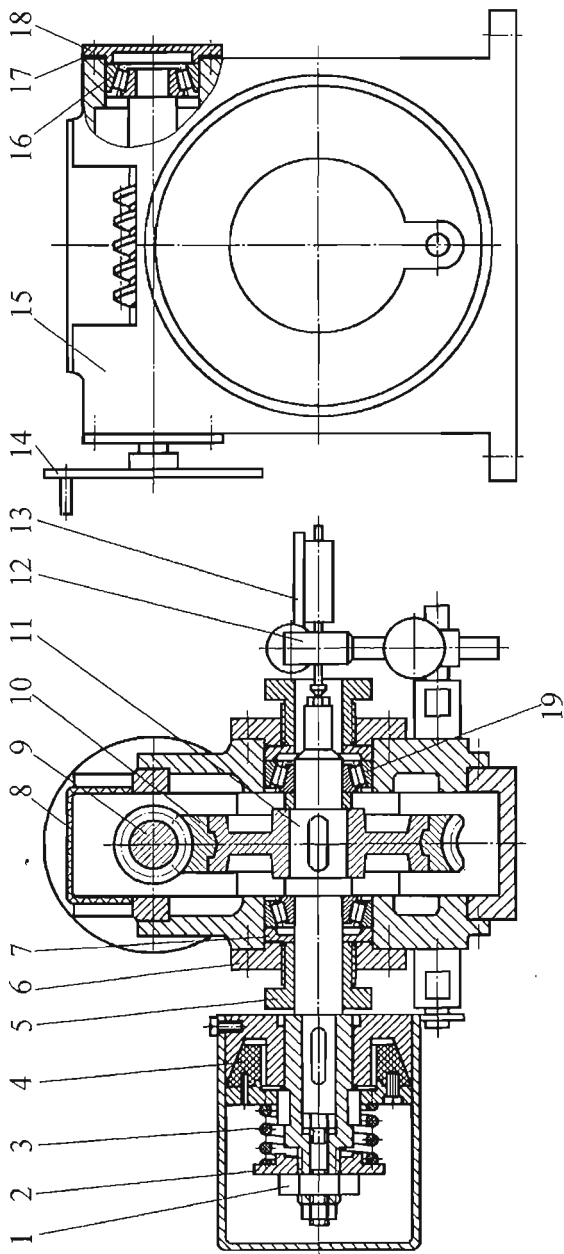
Лабораторная установка для регулировки зацепления червячной передачи
